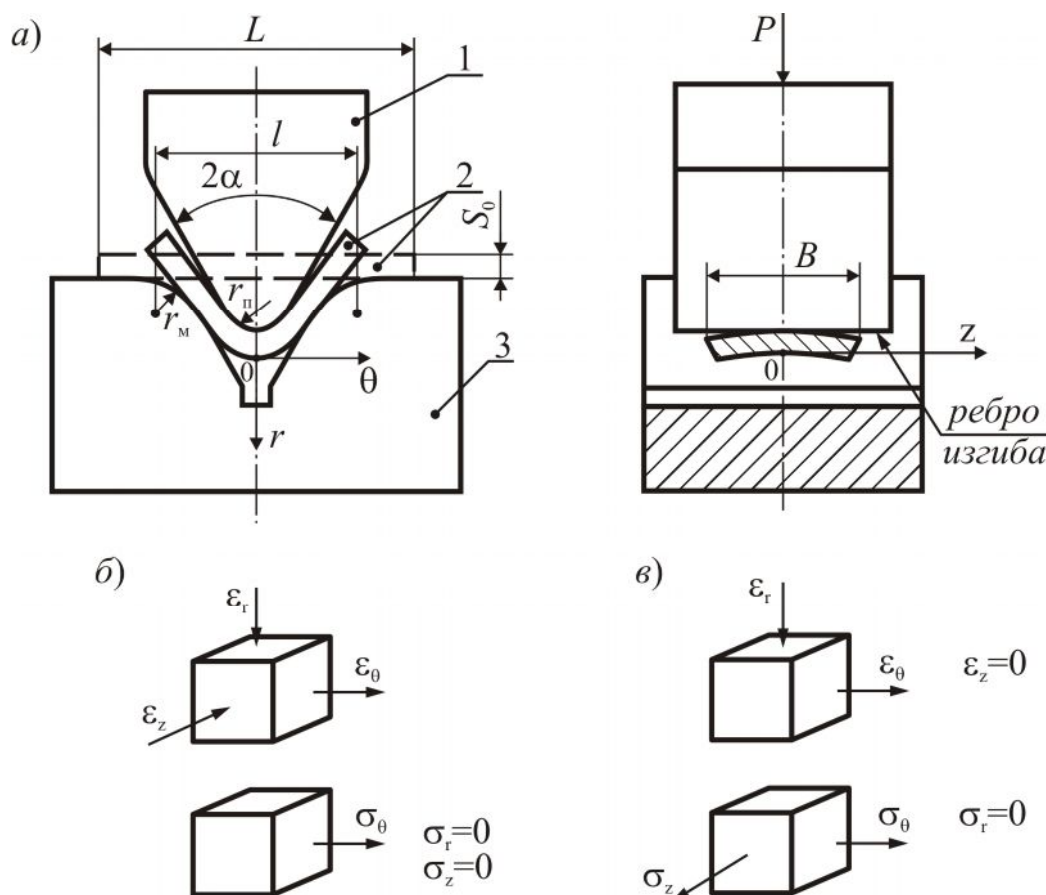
Схема изгиба в штампе (а) и схемы деформации и напряжений материального элемента в зоне точки 0 наружной поверхности узкой (б) и широкой (в) листовых заготовок: 1 – пуансон; 2 – заготовка; 3 – матрица
